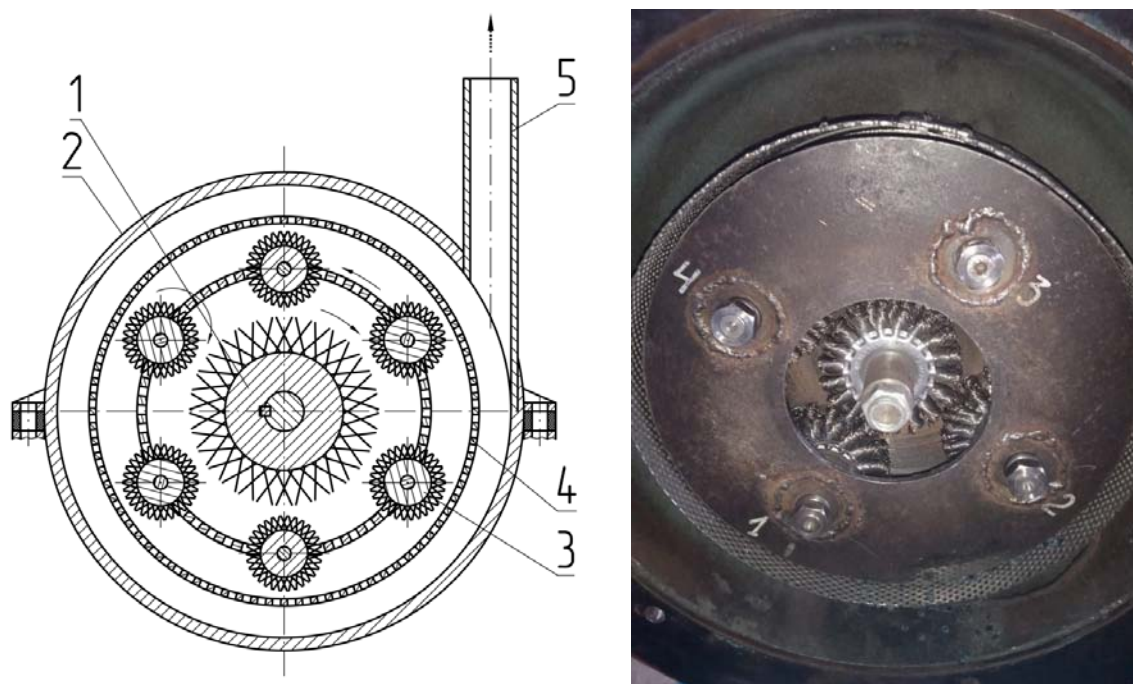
Камера роторно-центробежного агрегата с иглофрезерными рабочими органами:
